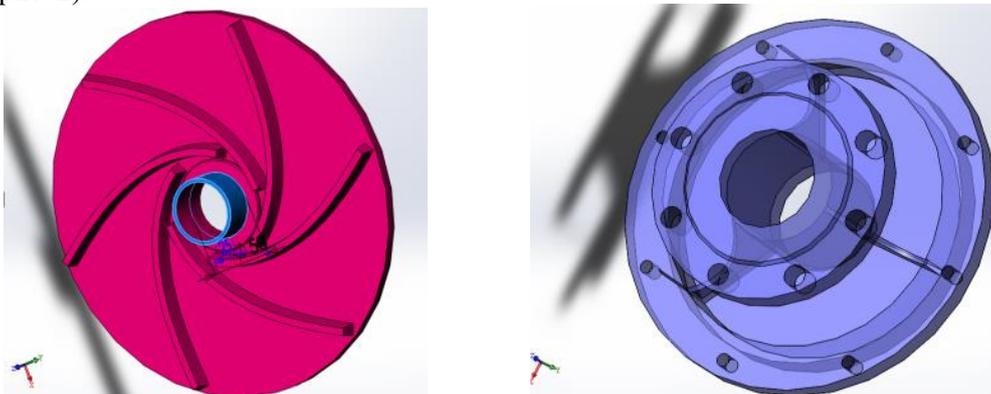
Разработанные конструкции рабочего колеса и сальниковой втулки
